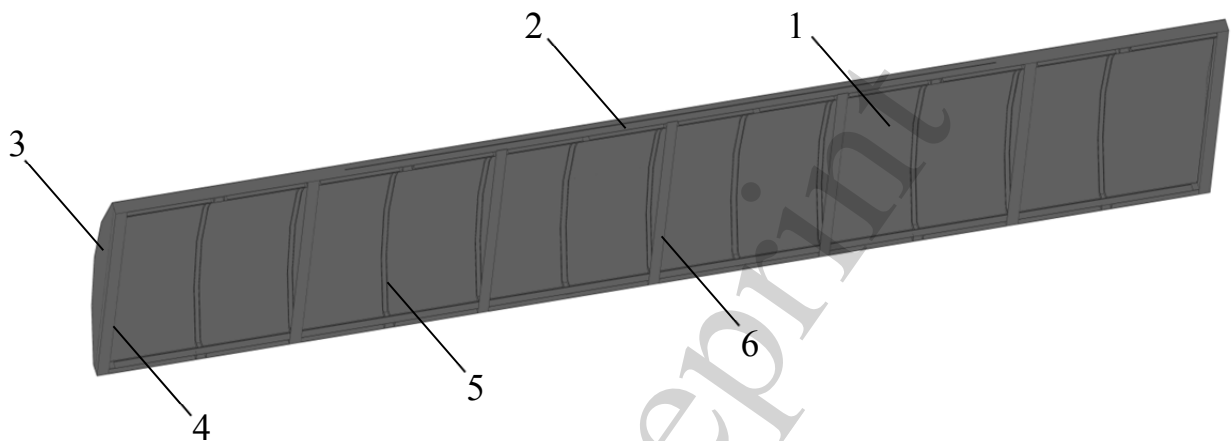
Просторова модель зйомного даху: 1 – обшивка; 2 – бічна повздовжня балка; 3 – торцевий лист обшивки; 4 – торцева поперечна балка; 5 – дуга поперечна; 6 – проміжна поперечна балка
